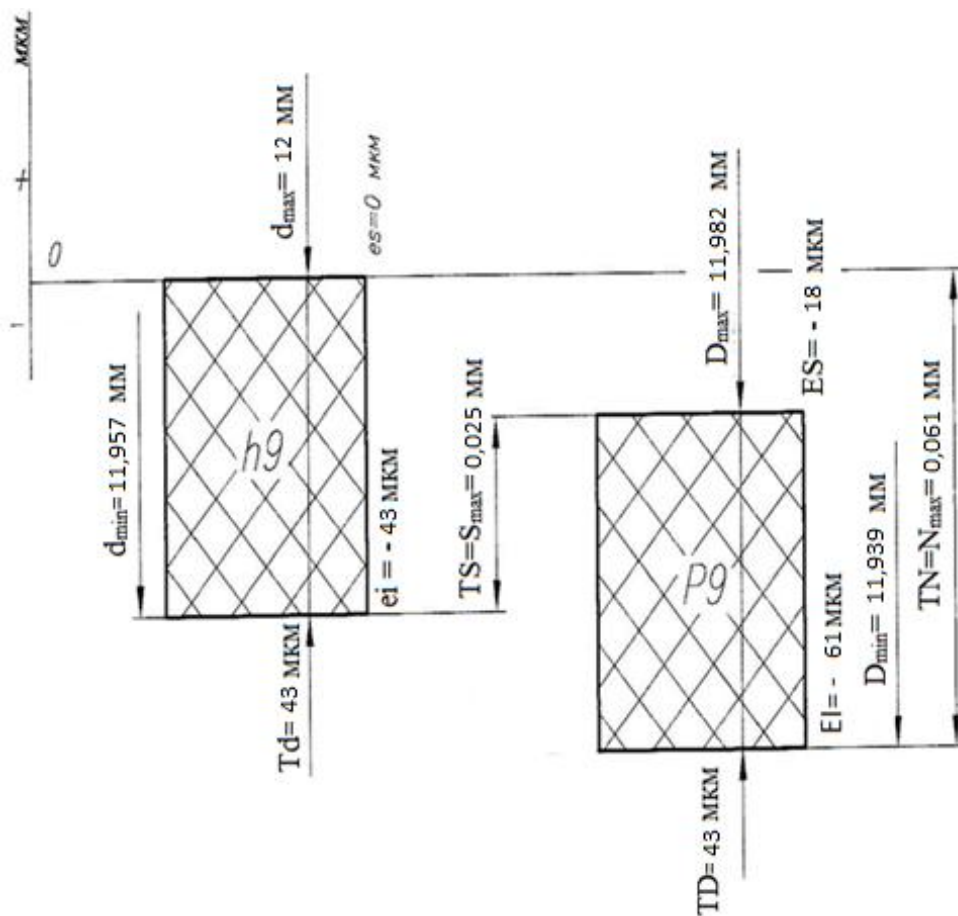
Расположение полей допусков шпонки и паза вала для переходной посадки
